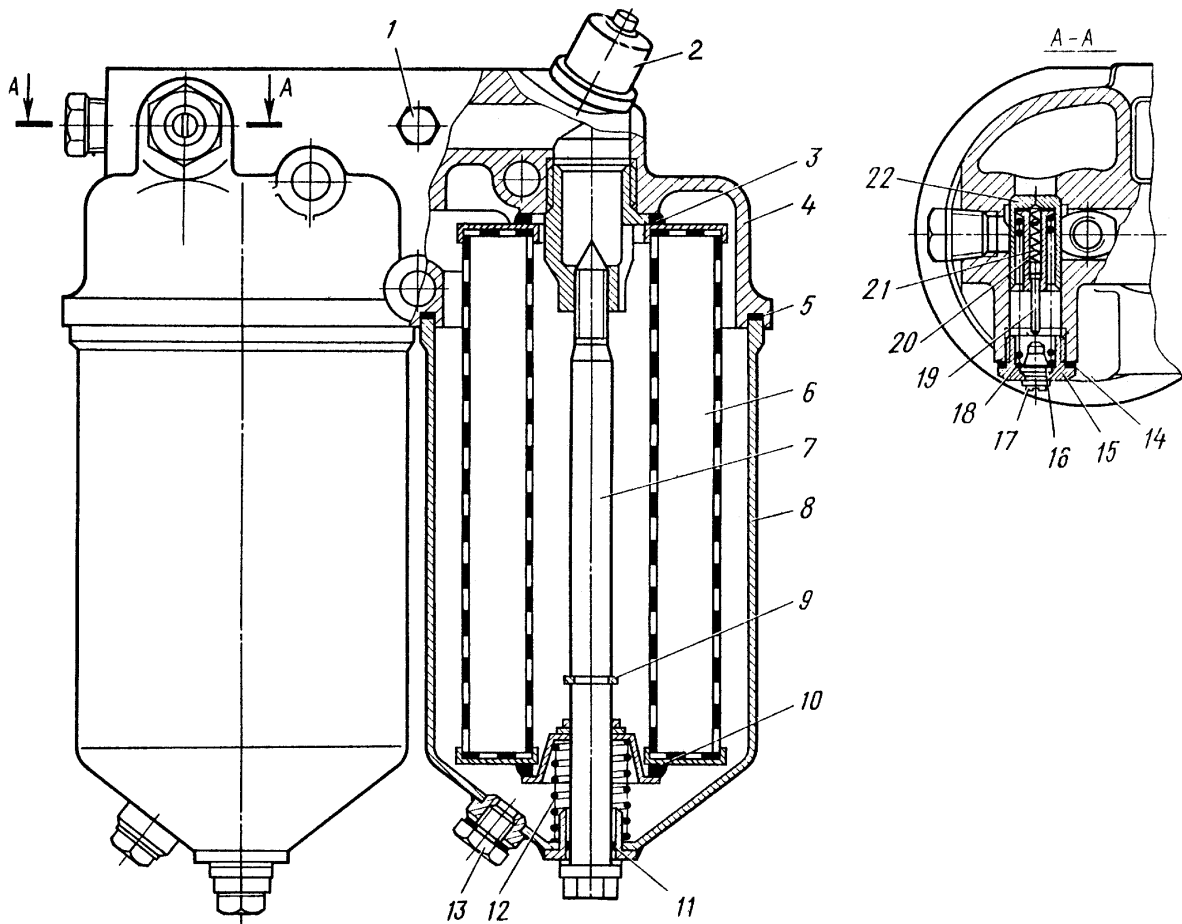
Полнопоточный фильтр тонкой очистки масла со сменными объемно-абсорбирующими элементами:
